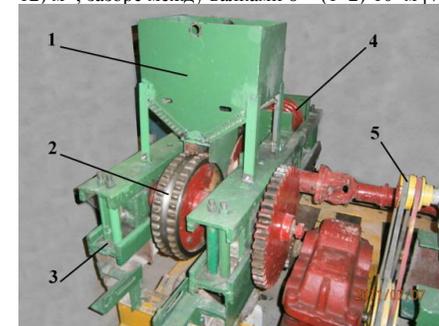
Пресс-валковый агрегат для брикетирования порошкообразных и вязкопластичных техногенных материалов: 1 - приёмный бункер шихты с уплотняющими устройствами; 2 - формующие элементы желобково-зубчатого типа; 3 - рама пресс-валкового агрегата; 4 - узел амортизации валков; 5 - привод пресса
